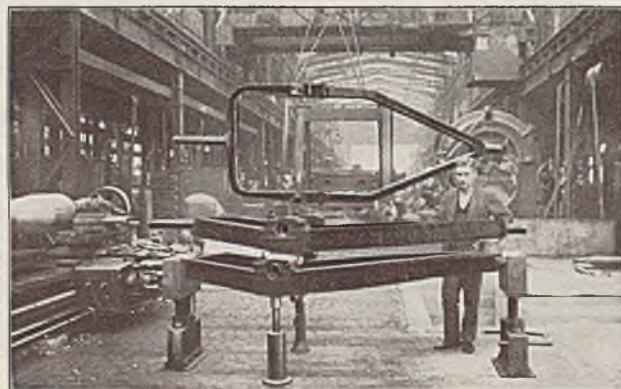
Bülgel für Drahtseilwickelmaschinen
